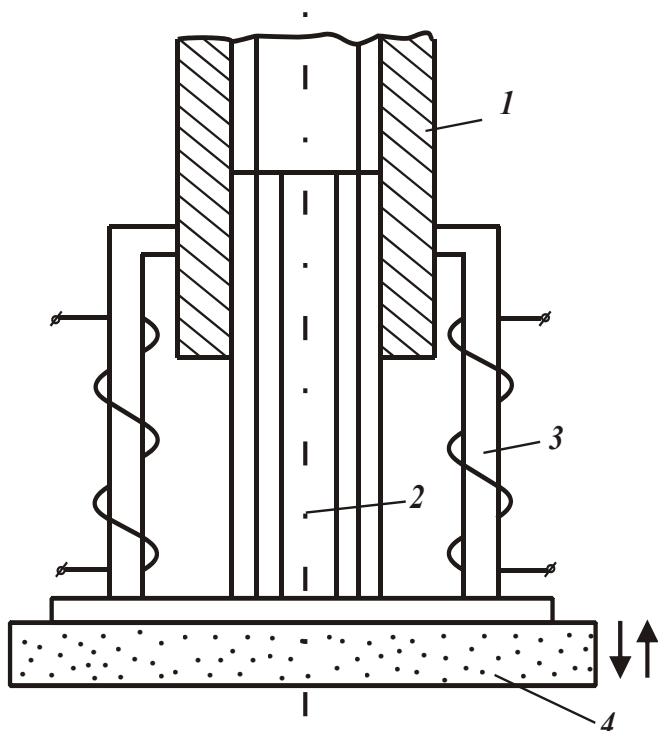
Магнестрикционный вибратор: 1 – шлицевая втулка; 2 – шлицевой вал, приваренный к цилиндрическому основанию; 3 – преобразователь с обмоткой, сердечник которого замыкается на шлицевой втулке и основании с помощью сварки; 4 – круг, установленный на основание вибратора с помощью смол или клеев.
